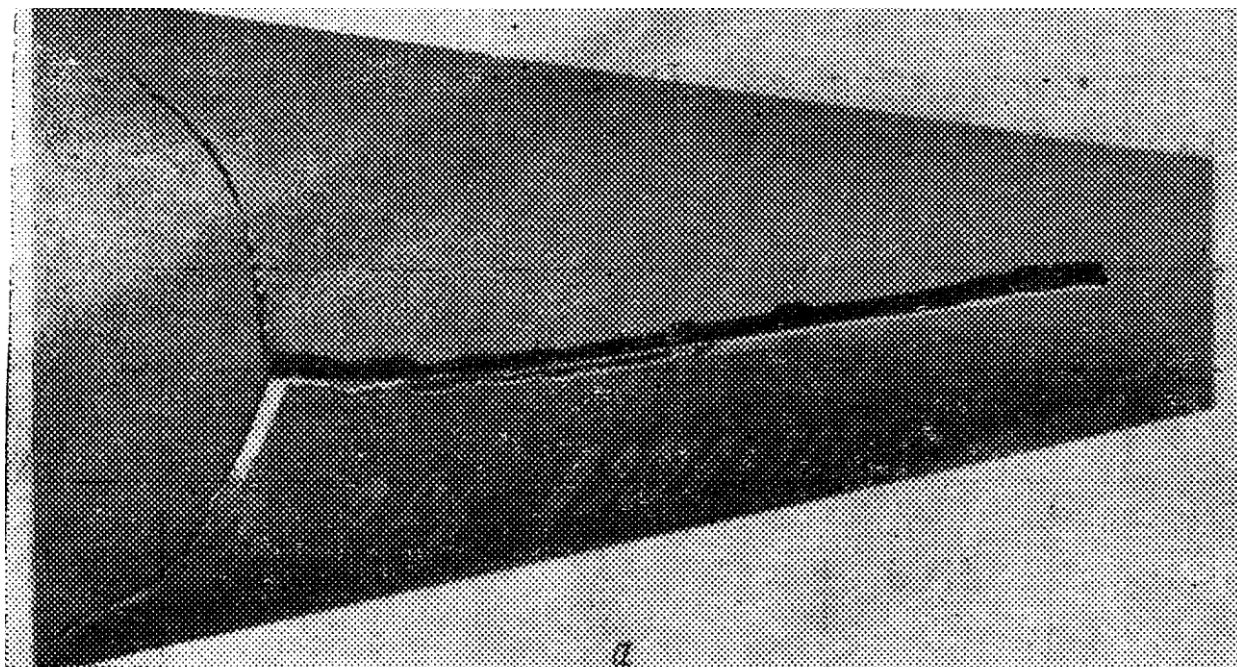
Обсадная труба лопнувшая при опрессовке.
